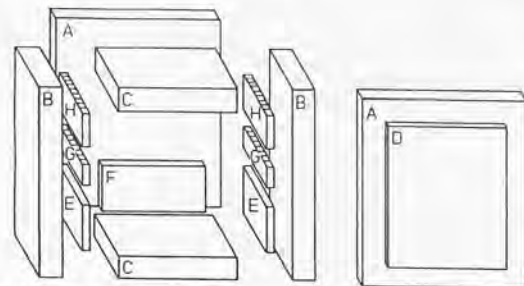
Zusammensetzung des selbstgebauten Brutschranks: «Explosionszeichnung» des Styroporgehäuses (links) sowie der Tür (rechts) ohne Inneneinrichtung
